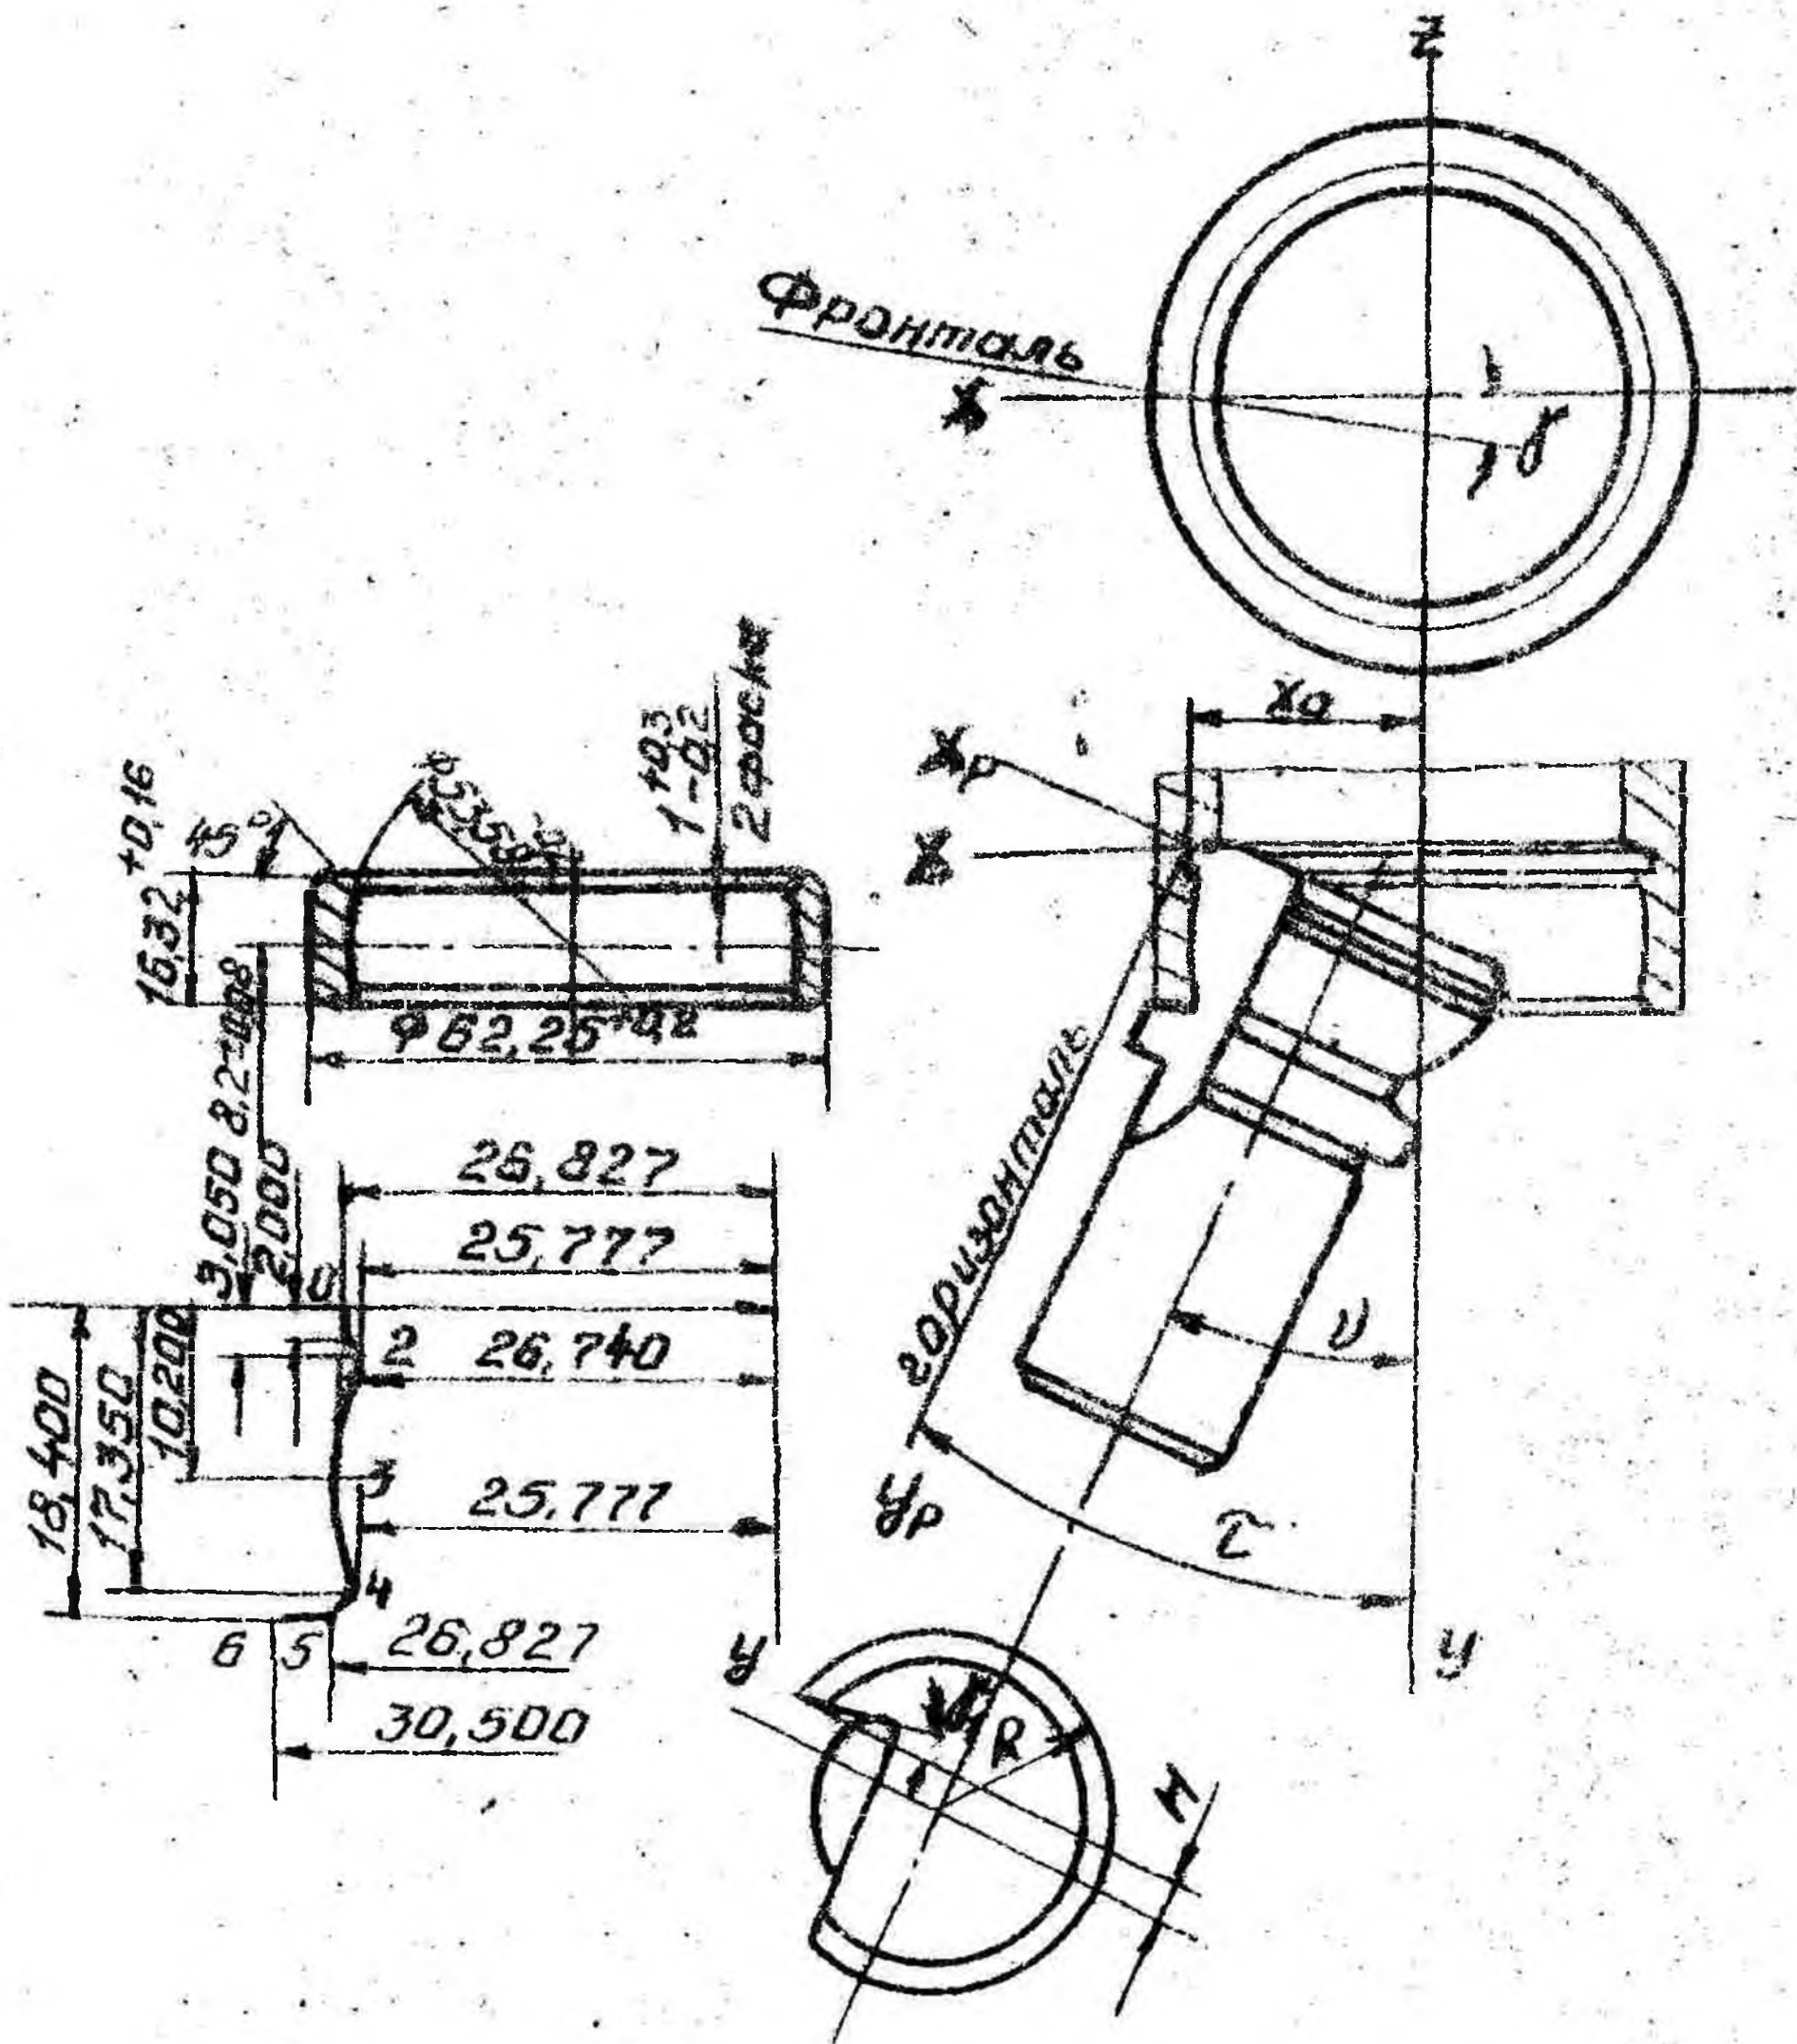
Круглый фасонный резец для обработки кольца подшипника 1206/01
